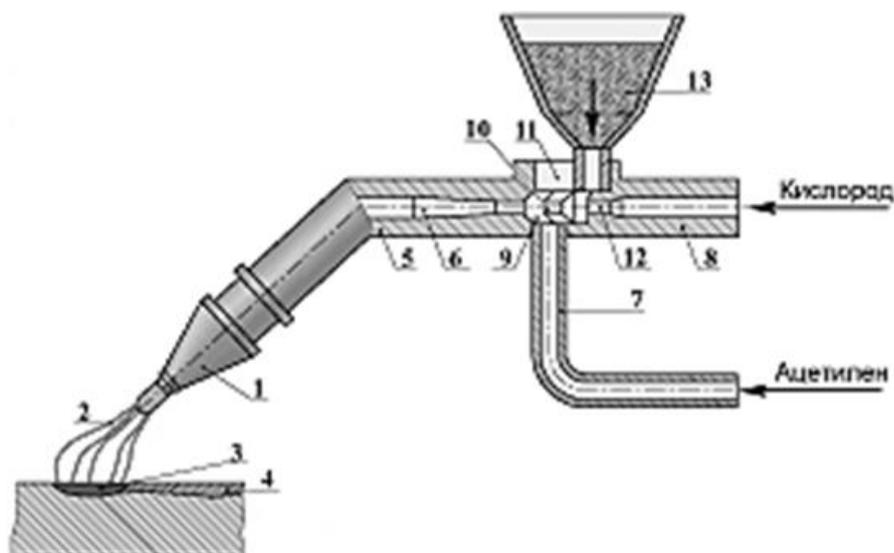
Устройство сварочной горелки для наплавки порошка.
